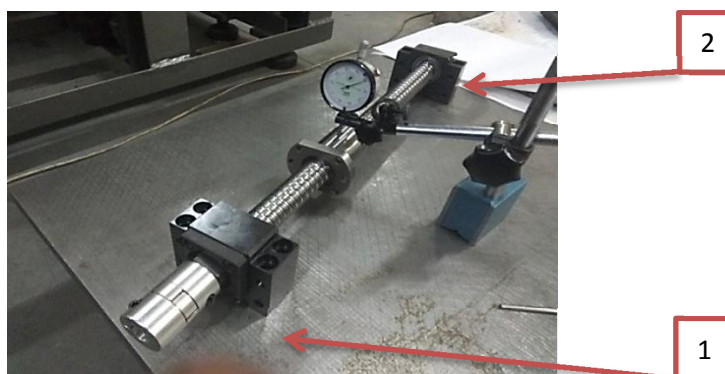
Ходовой винт, установленный в подшипниковые опоры: 1- жесткая опора, 2 – плавающая опора
